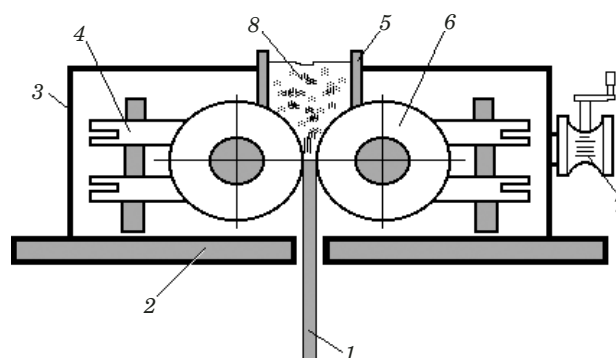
Схема рабочей прокатной клетки УЭИС: 1 — спеченная лента; 2 — станина; 3 — герметичный металлический кожух; 4 — электрические контакты; 5 — бункер для порошка; 6 — валки-электроды; 7 — червячно-нажимное устройство регулирования зазора между валками; 8 — порошок
